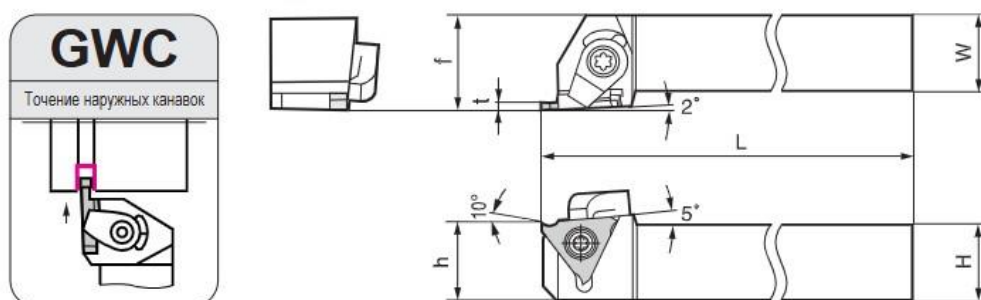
Державка GWC R 2525-25 [1, с. 172]
